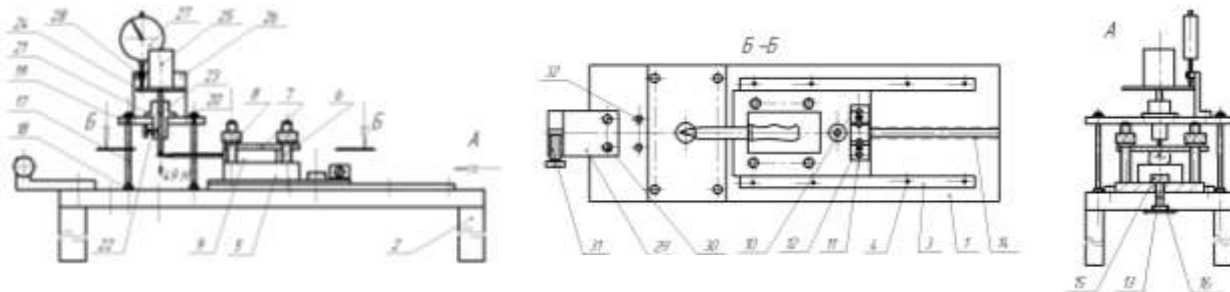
Схема налагодження пристрою для визначення міцності та пружності конструкції клинка: 1 – корпус; 2 – ніжки; 3 – напрямні; 4 – гвинти; 5 – рухомий столик; 6 – шпильки; 7 – пластина; 8 – гайки; 9 – руків'я; 10 – опорний елемент; 11 – гвинт; 12 – гвинт регулюючий; 13 – болт стопорний; 14 – Т-подібний паз; 15 – гайка; 16 – пластина; 17 – стойка; 18 – гайка; 19 – пластина; 20 – гайка; 21 – напрямна; 22 – гвинт стопорний; 23 – вимірювальний штир; 24 – пластина; 25 – вага; 26 – опора; 27 – вимірювальний прилад; 28 – гвинт; 29 – кронштейн; 30 – гвинт; 31 – гвинт; 32 – різьбові отвори
